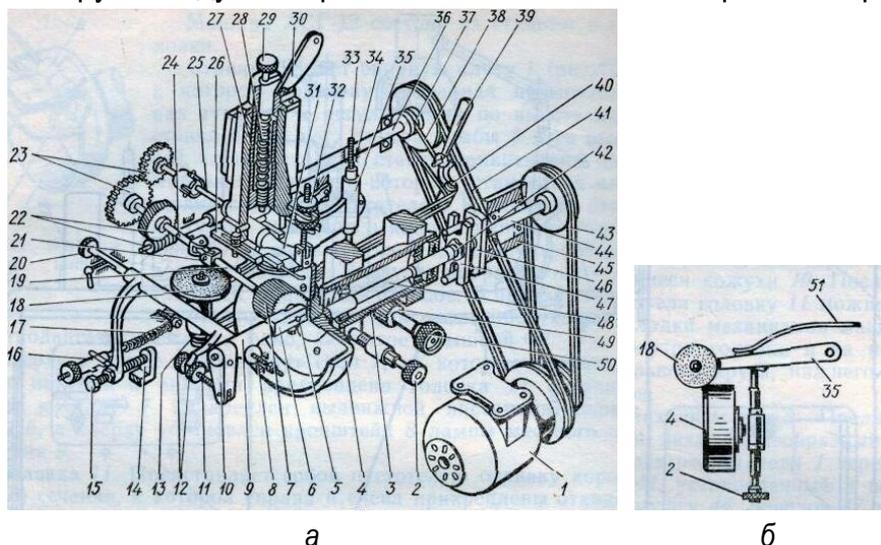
Схемы головки машины АСГ-12 (а) и заточки ножа (б)
